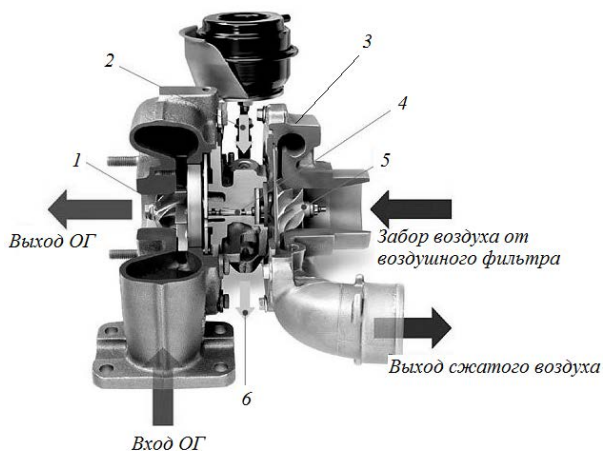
Турбокомпрессор дизеля: 1 – турбина; 2 – канал подачи масла к подшипникам; 3 – корпус подшипников; 4 – вал ротора; 5 – компрессор; 6 – канал слива масла
